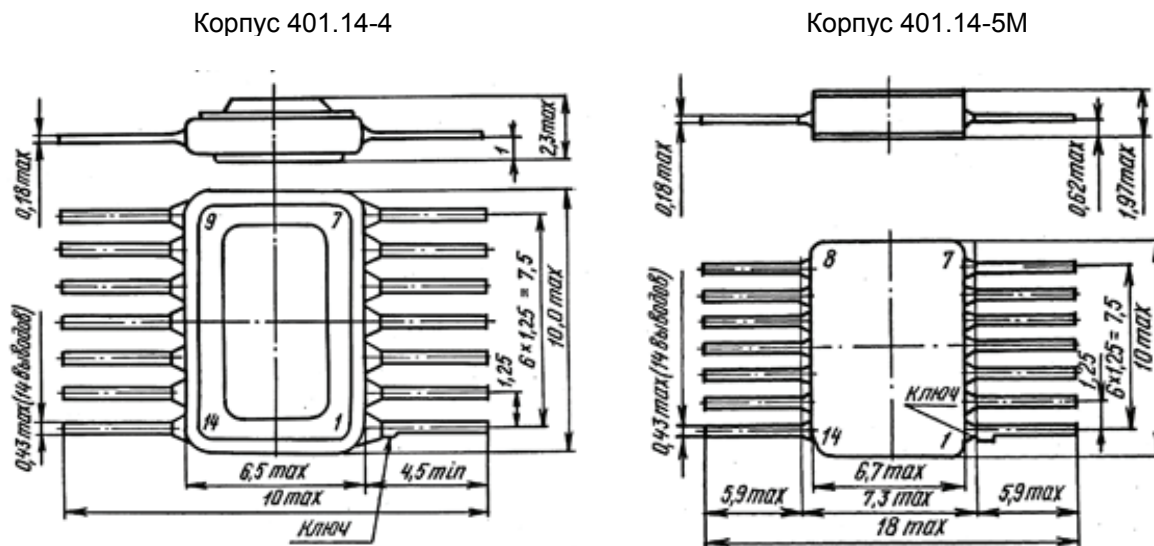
Габаритные чертежи корпусов 401.14-4 и 401.14-5M
